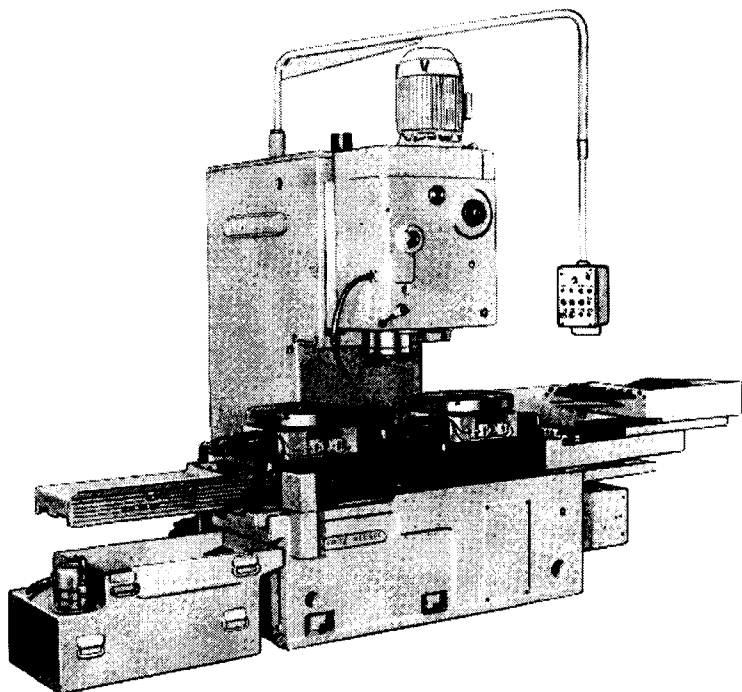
Продольно-фрезерный станок с двумя круглыми делительными столами
